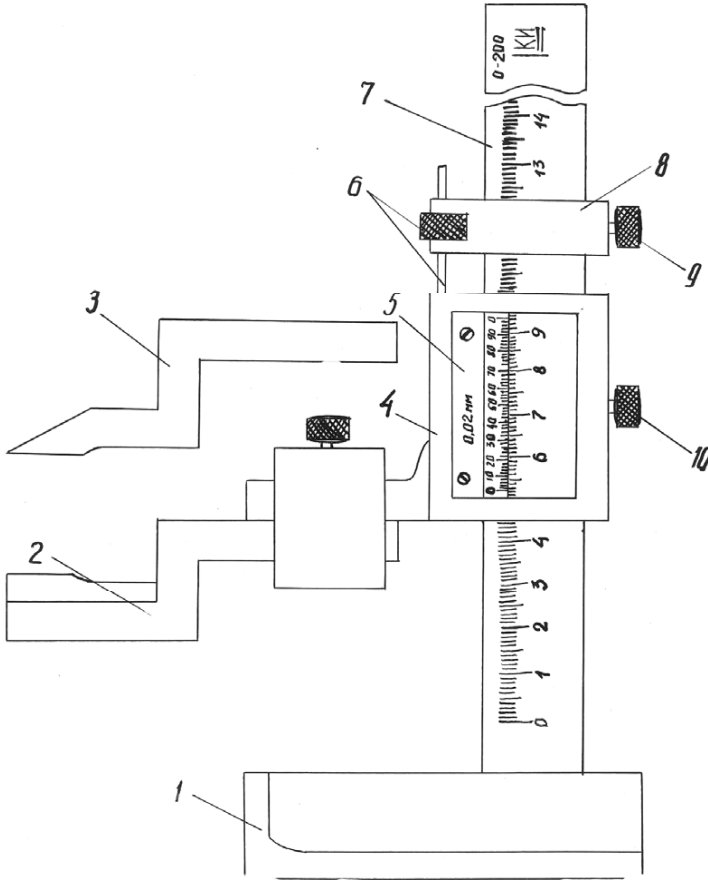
Штангенрейсмус: 1 – основа; 2 – вимірювальна ніжня розмітчна ніжка; 4 – рамка; 5 – ноніус; 6 – гвинт і гайка мікрометричної подачі; 7 – штанга; 8 – рамка мікрометричної подачі; 9 – затискач рамки мікрометричної подачі; 10 – затискач рамки.
